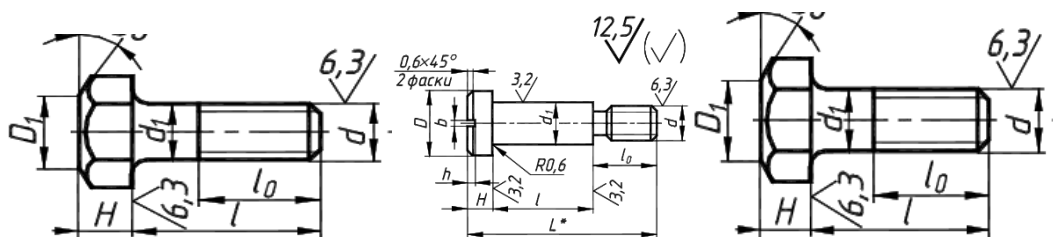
Форма и размеры концов болтов, винтов и шпилек
